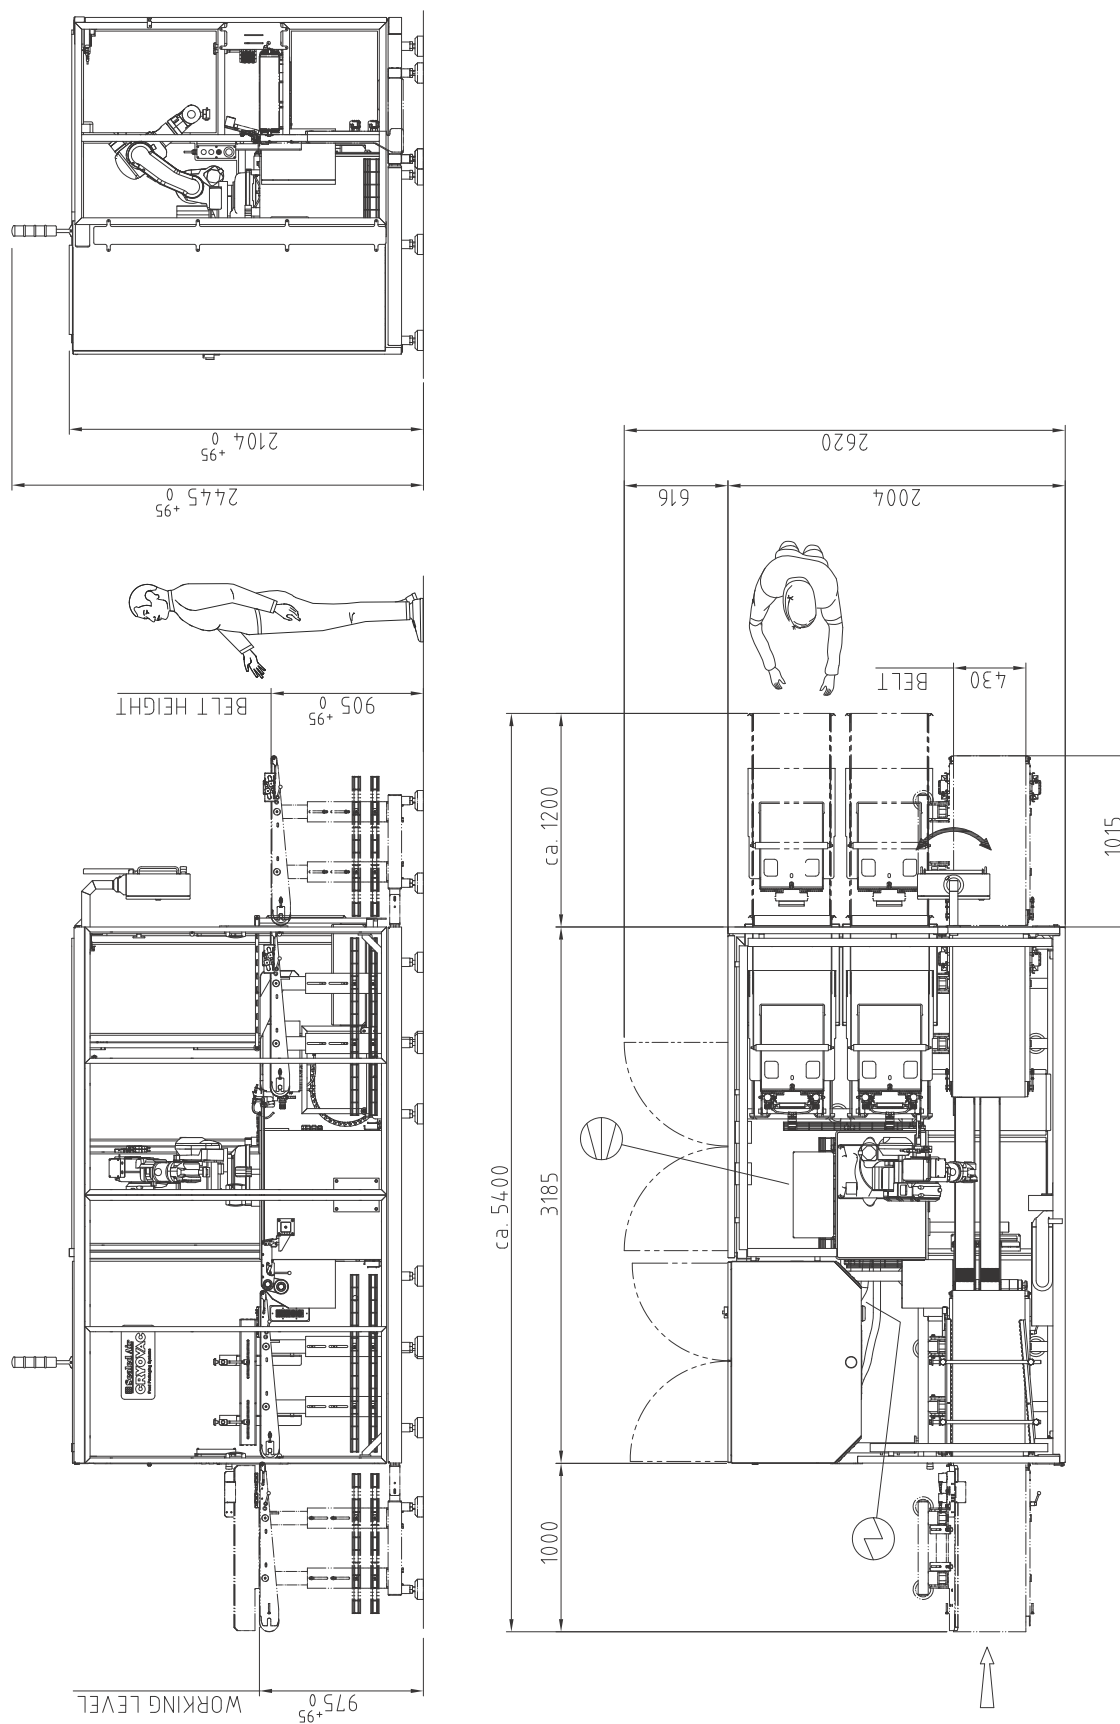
, Dimensiones LR (flujo del producto de izquierda a derecha)
